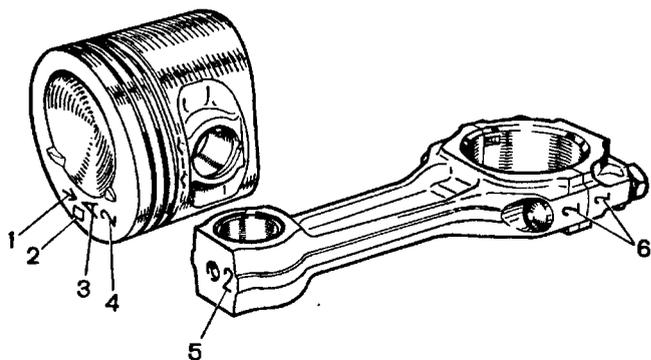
Маркировка поршня и шатуна: 1 - стрелка для ориентирования поршня в цилиндре; 2 - ремонтный размер; 3 - класс поршня; 4 - класс отверстия для поршневого пальца; 5 - класс шатуна по отверстию для поршневого пальца; 6 - номер цилиндра
